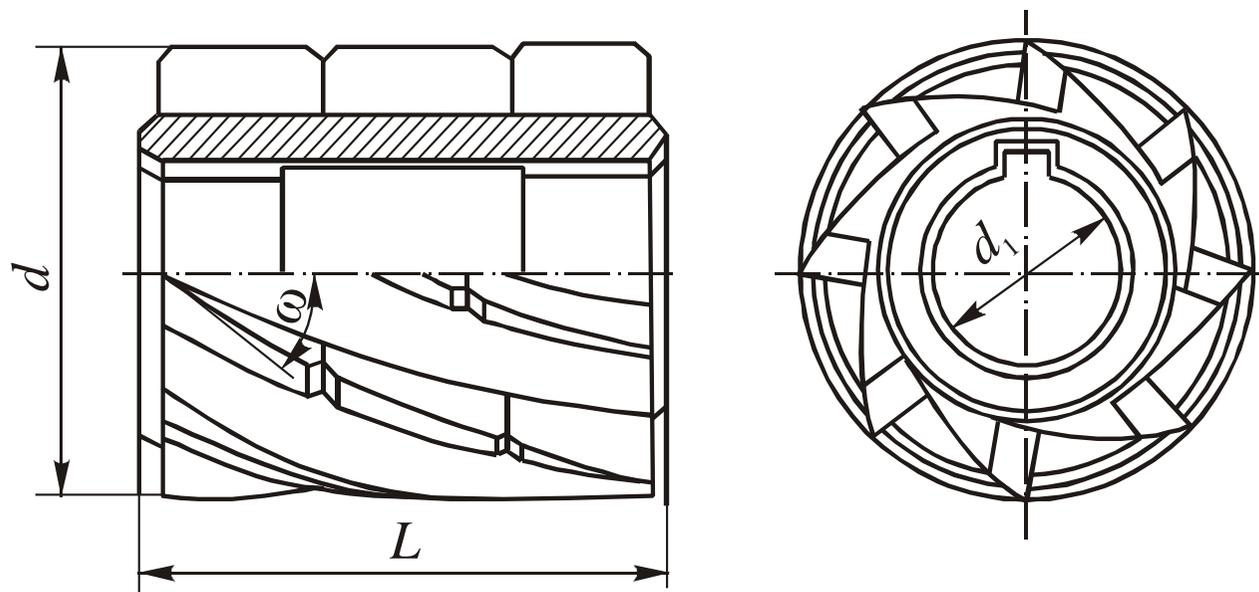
Цилиндрическая фреза, оснащенная напайными винтовыми твердосплавными пластинами
